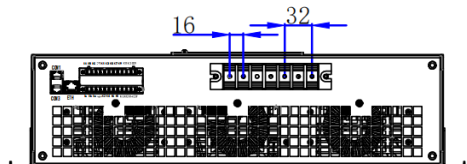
Розмірна схема модуля стійкового типу 30 кВАр / 35А
